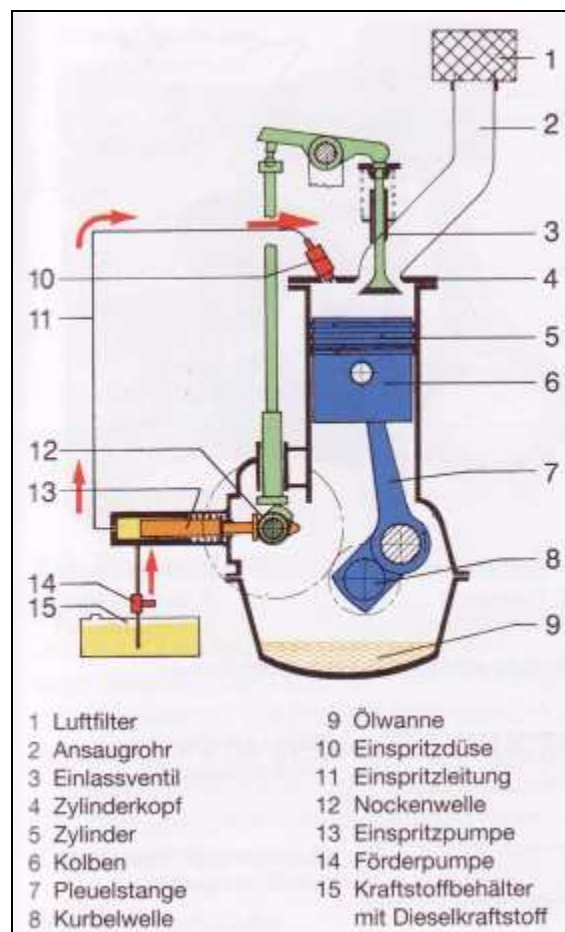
Prinzipskizze eines Dieselmotors mit Benennung der Komponenten; Quelle: [Q 39]
